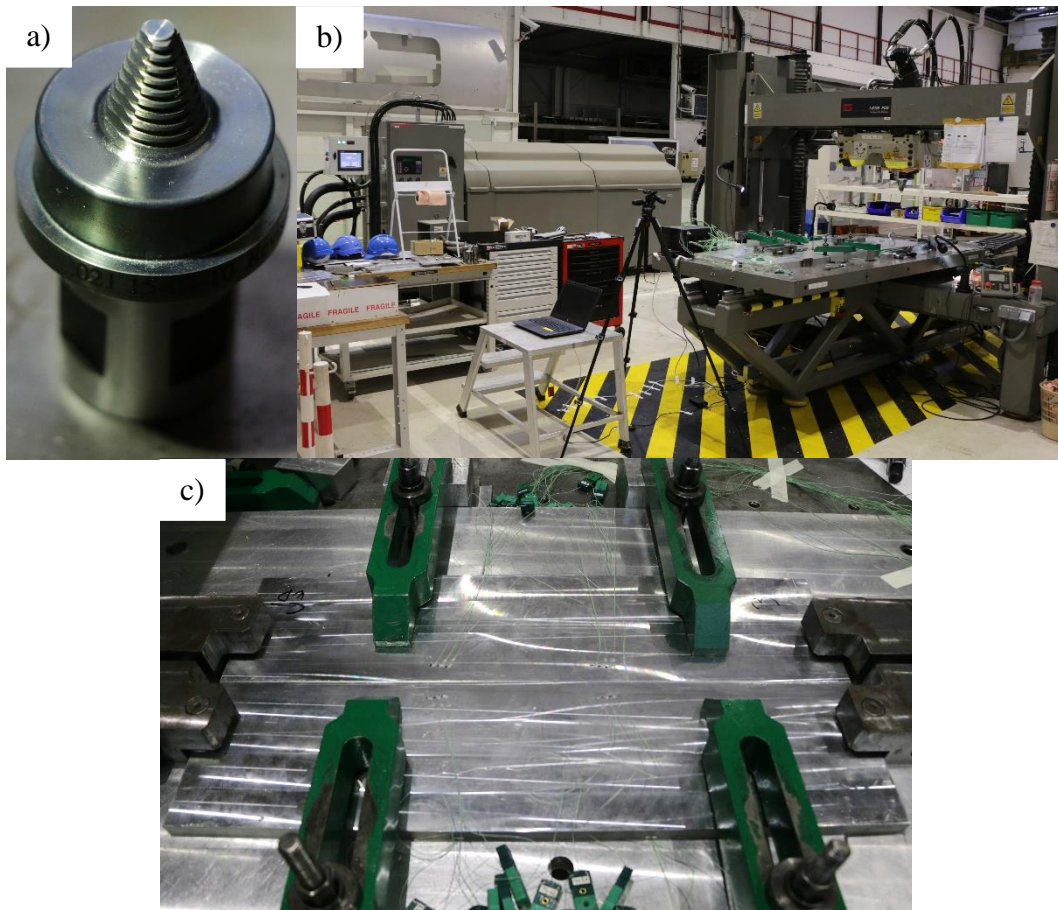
a) Outil utilisé pour le soudage, b) Environnement de soudage avec le groupe hydraulique à gauche et le portique de soudage à droite, c) bridage des plaques soudées avec les deux tire-forts aux extrémités des plaques
